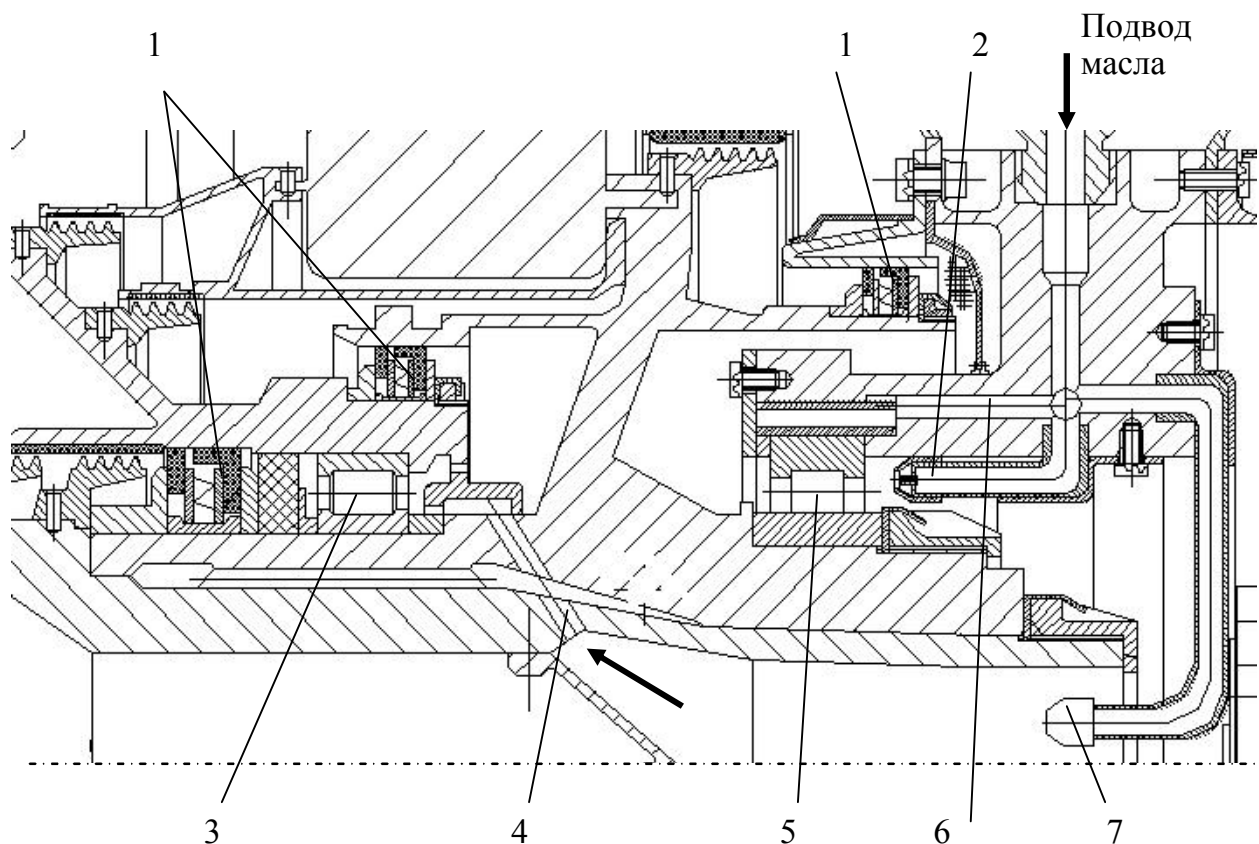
Смазка опор турбины ТРДДФ: 1 – контактные уплотнения; 2 – форсунка подачи масла к заднему подшипнику; 3 – межвальный подшипник; 4 – канал подвода масла к межвальному подшипнику; 5 – основной подшипник; 6 – канал подвода масла к масляному демпферу; 7 – форсунка подачи масла к межвальному подшипнику
